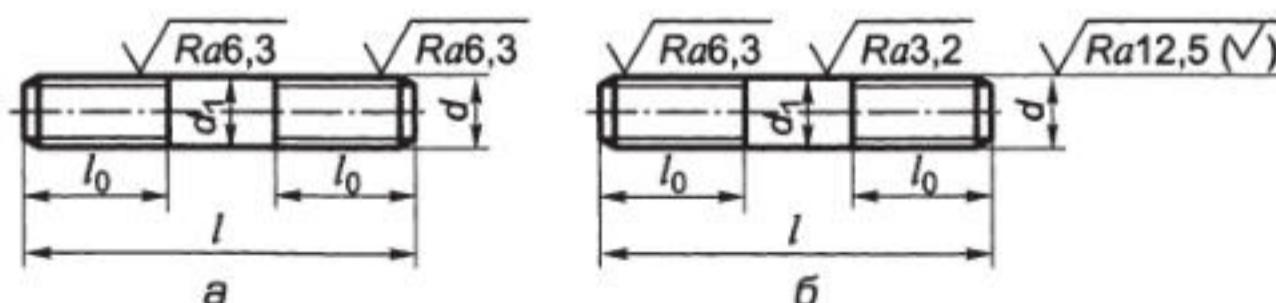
Шпильки общего применения классов точности В (а) и А (б) для деталей с гладкими отверстиями
